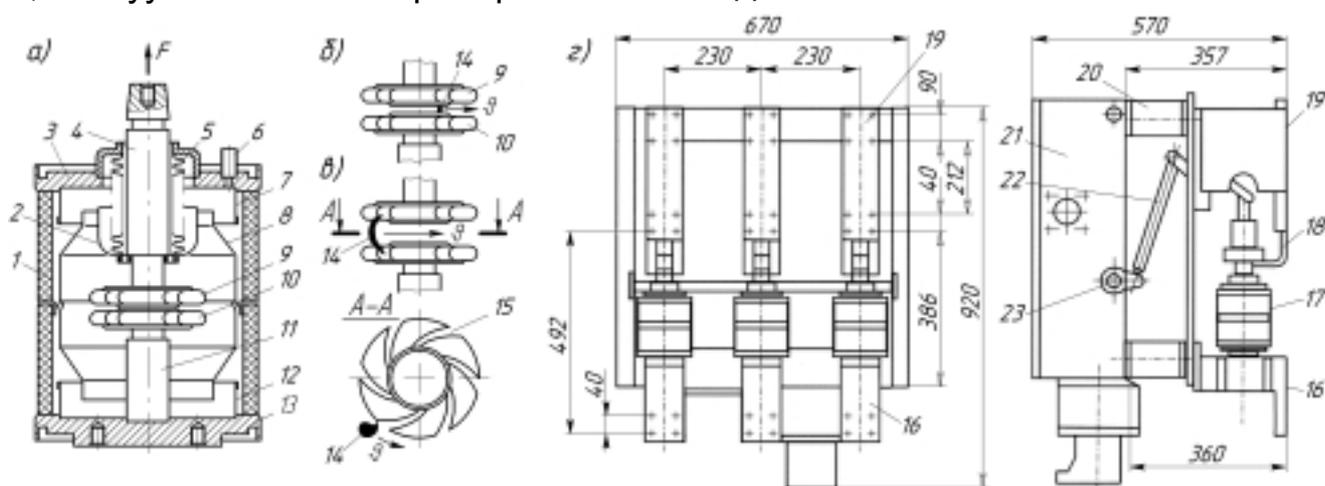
Вакуумный выключатель типа ВВПТ-10: конструкция вакуумной камеры (разрез) (а), метод гашения дуги между контактами камеры (б, в) и габаритные размеры выключателя (г)
